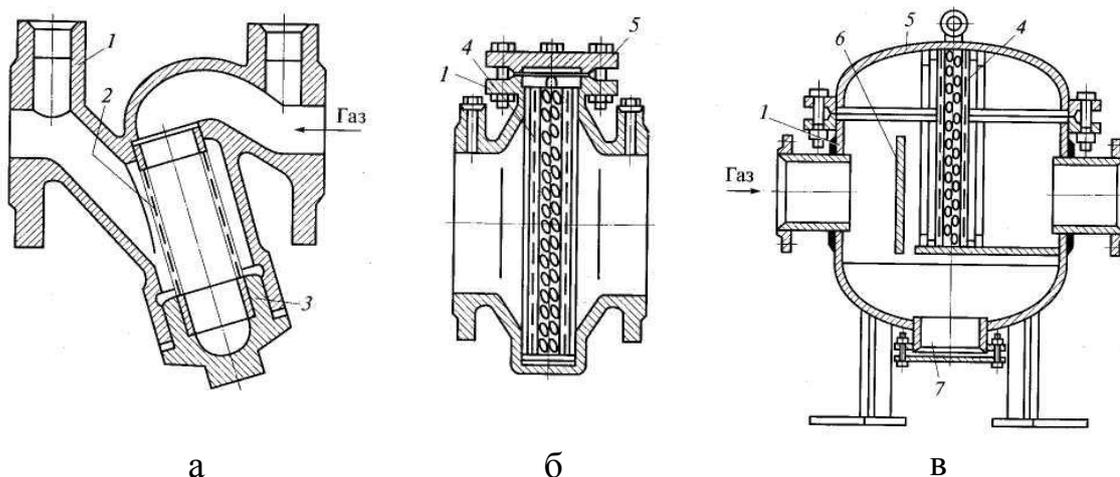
Газовые фильтры: а – угловой сетчатый; б – волосяной; в – сварной; 1 – корпус; 2 – обойма; 3 – пробка; 4 – кассета; 5 – крышка; 6 – отбойный лист; 7 – люк для чистки.
